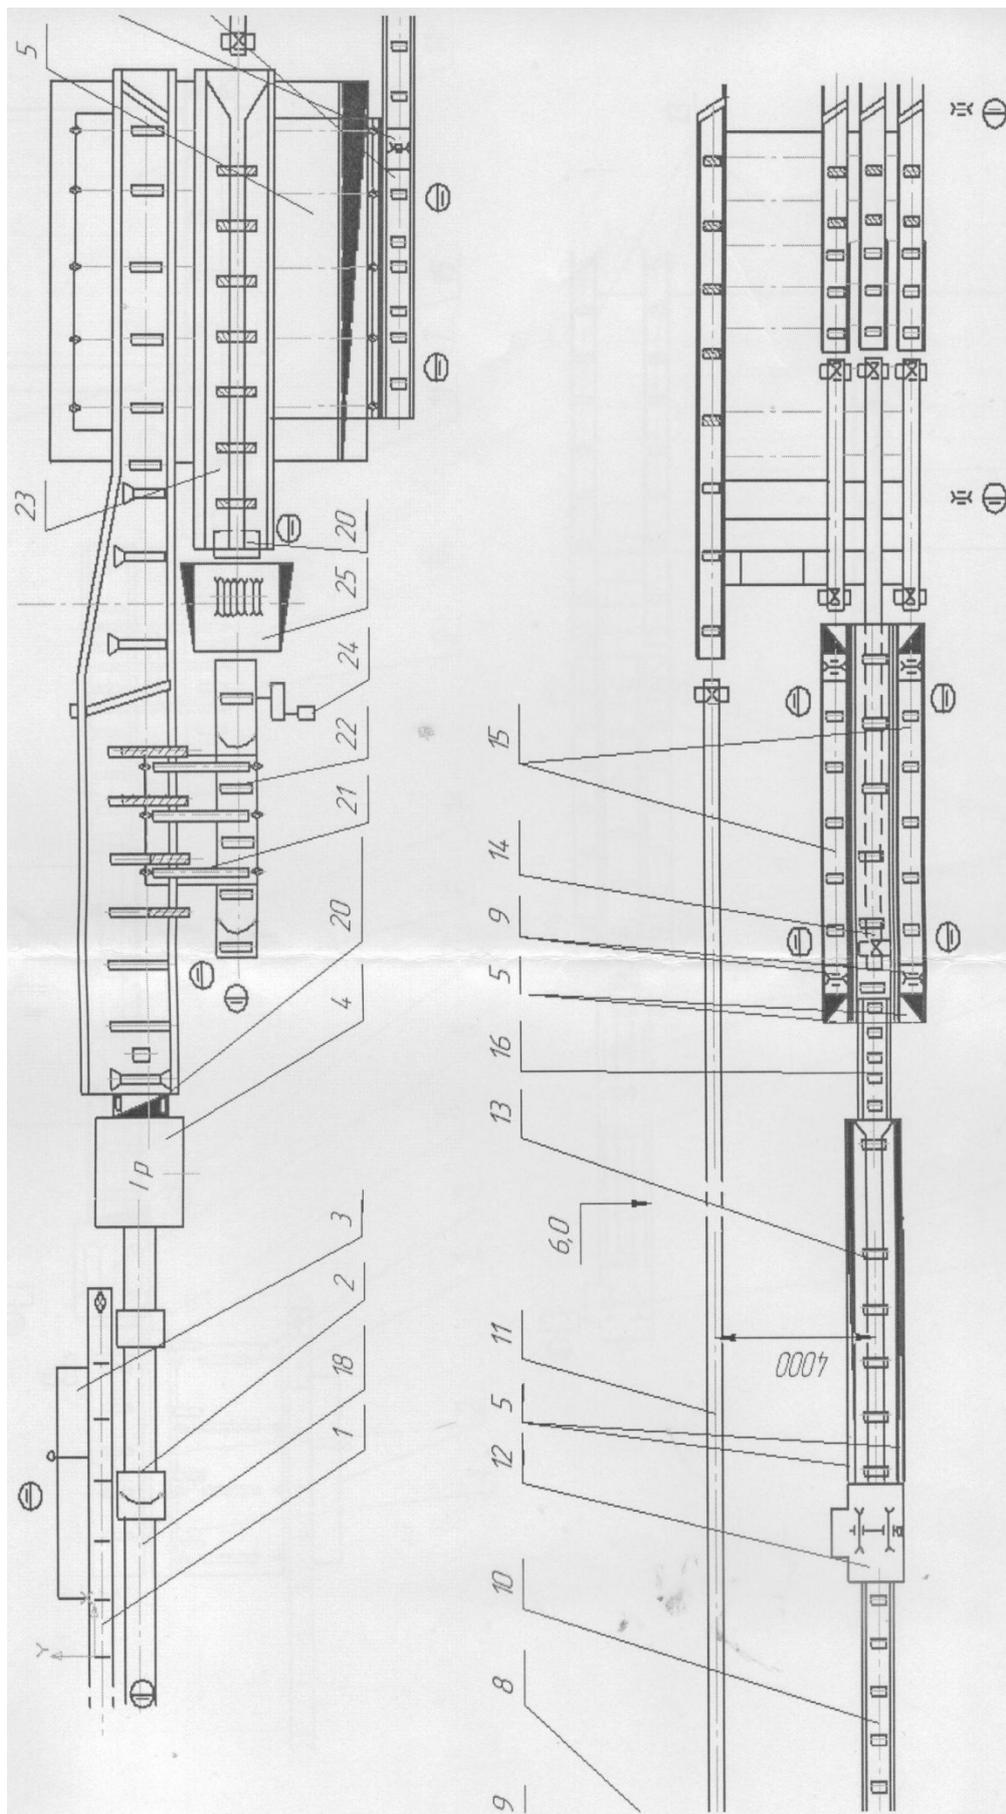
План второго этажа лесопильного цеха с двухэтажными лесопильными рамами: 1 – бревнотаска Б22У-1; 2 – передирамная тележка ПРТ-8; 3 – сбрасыватель СБР4-2; 4 – лесопильная рама 2Р75-1; 5, 20 – люки; 6 – поперечный конвейер ТЦП-5; 7, 8 – ленточные конвейеры КЛ-50; 9 – роликовый конвейер; 10 – приводной ролянг; 11 – ленточный конвейер КЛ-50; 12 – обрезающий станок Ц2Д-5А; 13 – рейкоотделительное устройство; 14 – приемный стол; 15, 16 – ролянг неприводной; 17 – ролики; 18 – рельсовый путь; 19 – упор; 21 – брусоперекладчик; 22 – впередирамный ролянг; 23 – позадирамный ролянг; 24 – привод; 25 – круглопильный многопильный станок
